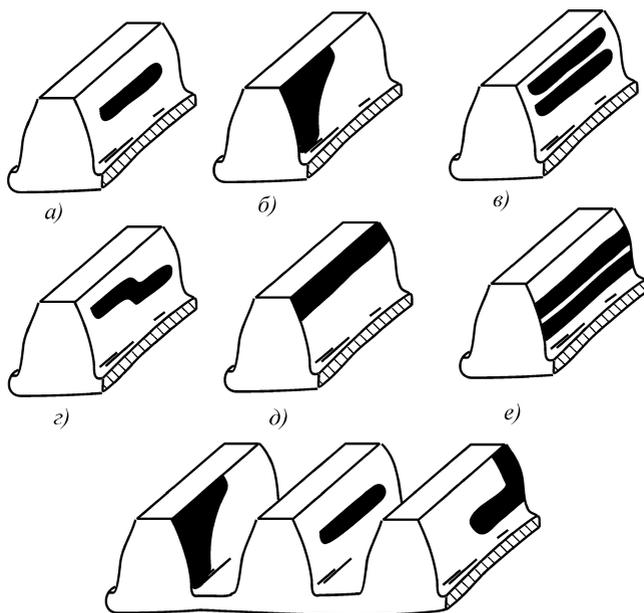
Соответствие пятен контакта и качества сборки цилиндрических зубчатых передач:
